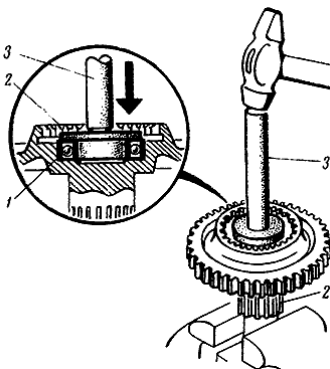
Запрессовка подшипника во вторичный вал КПП:
